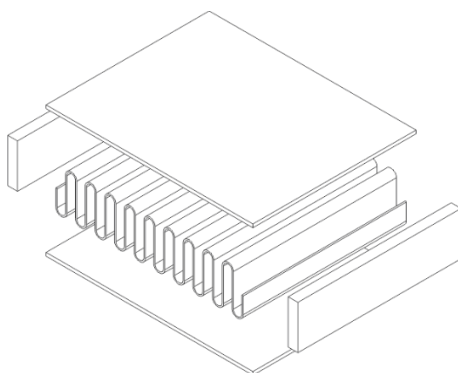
Ilustração de um trocador de calor placa aletada soldada por difusão [4].
